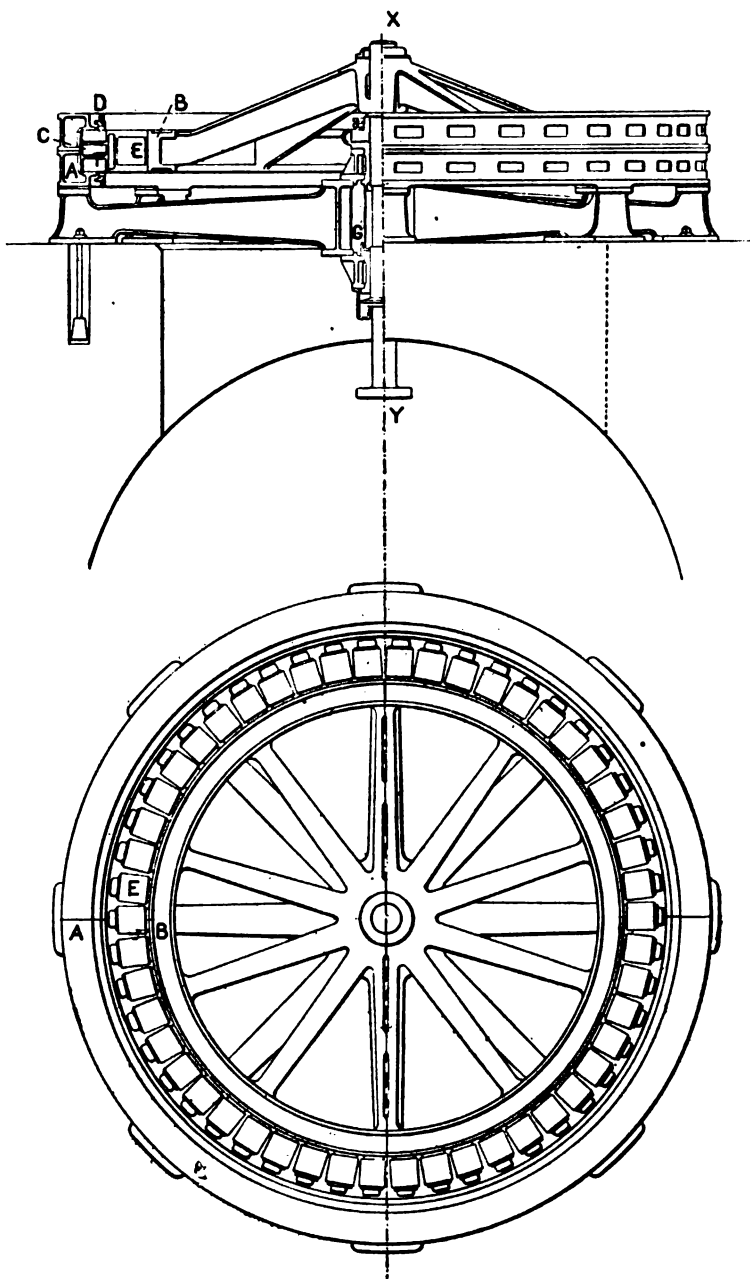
et 2. — Coupe et vue en plan d'un alternateur.
